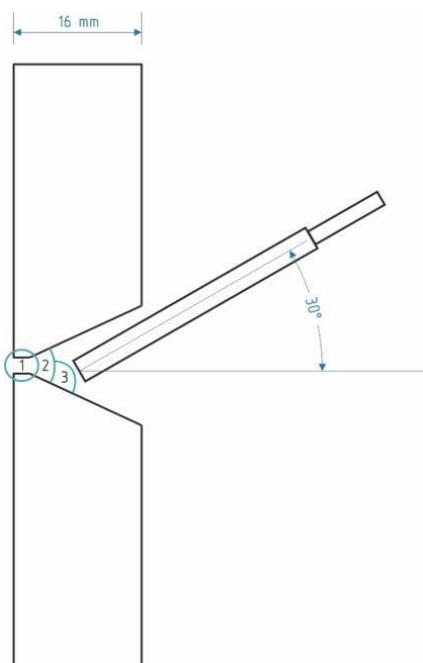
Профиль валика сварного шва и угол наклона электрода №3
